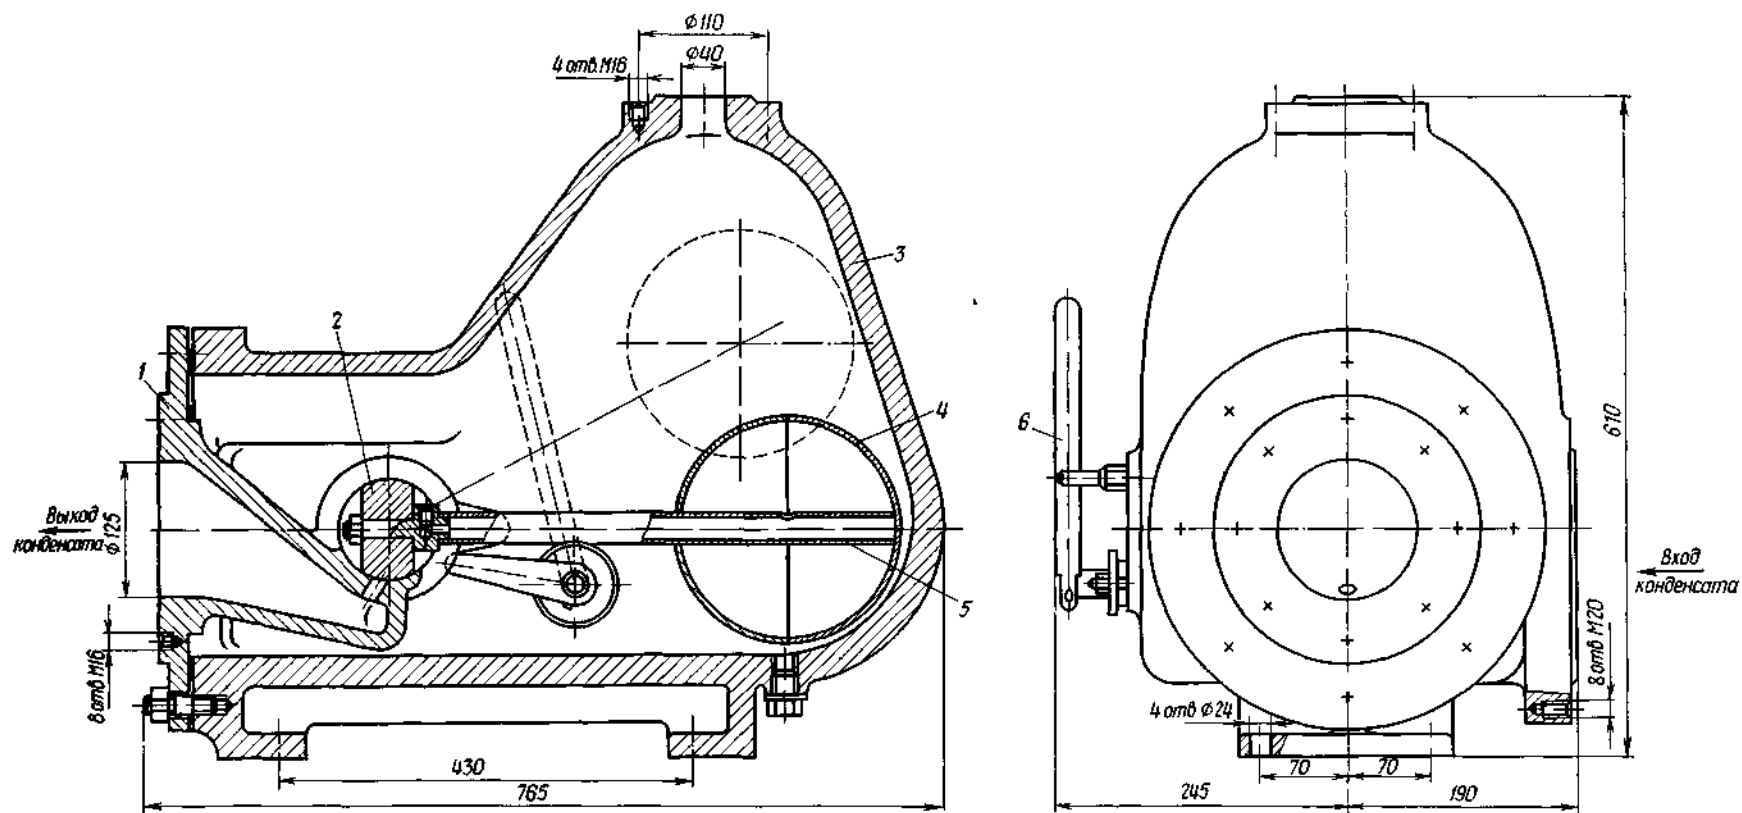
Конденсатоотводчик КГ-150/125  $D_y$  150/125  $p_y$  0,6 ... 1 МПа: 1 — патрубок отводящий; 2 — золотник, 3 — корпус; 4 — поплавок; 5 - штанга, 6 - рычаг
